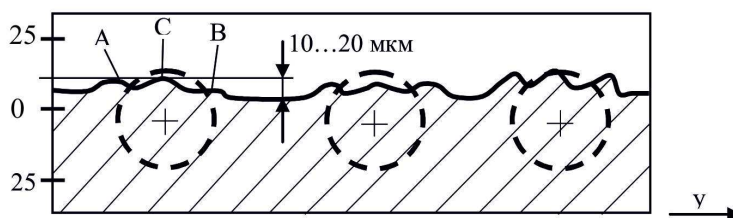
Формирование продольных выступов при обработке заготовки с бронзовыми вставками
